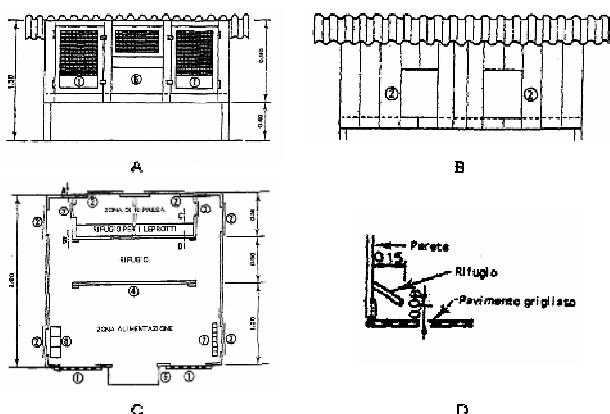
Prospetto e pianta de modello di gabbia di tipo “francese”. A, B, C: veduta anteriore, posteriore e dall’alto. D: particolare della porzione interna del nido
